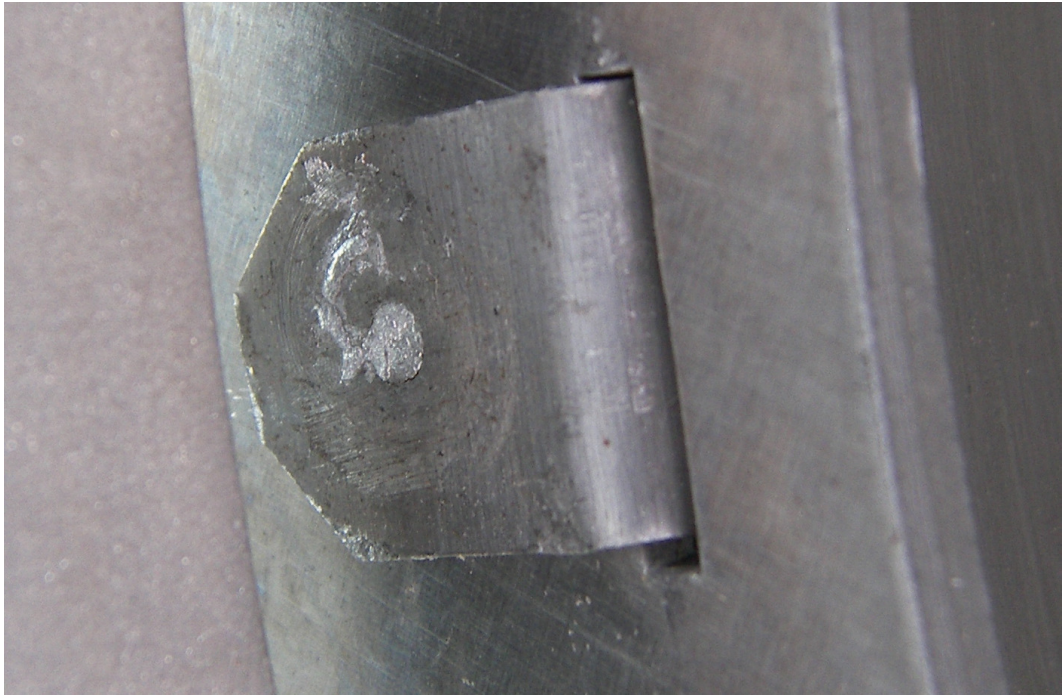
Detailaufnahme einer punktgeschweißten Lasche des Trommelrohres
